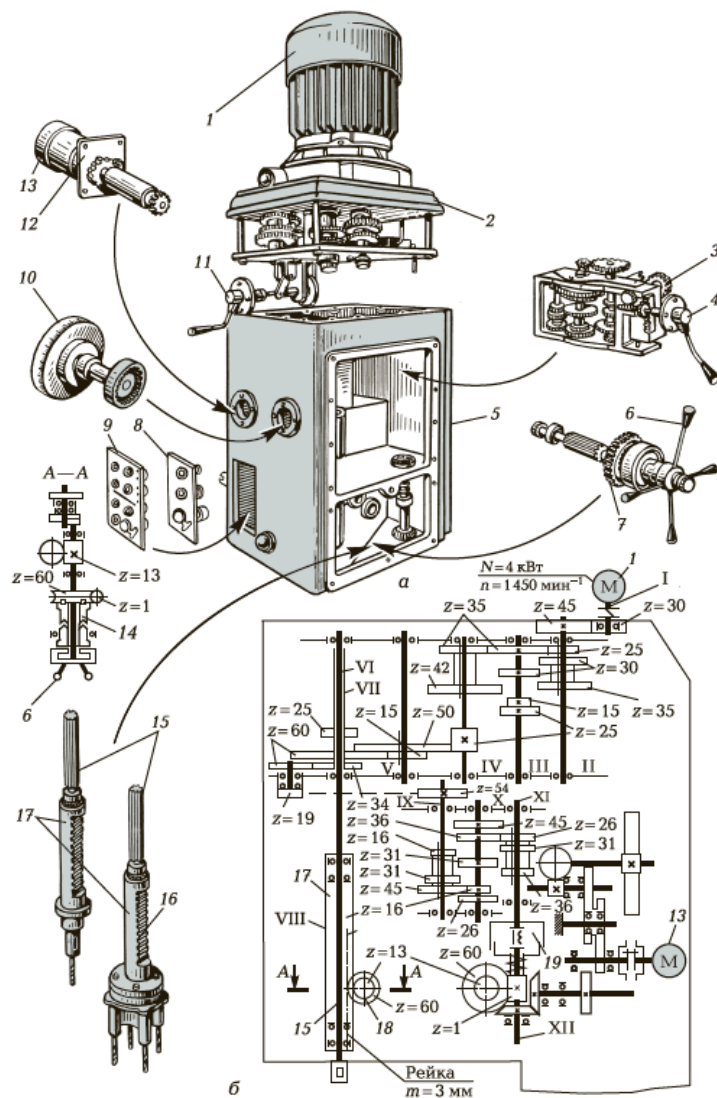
Сверлильная головка (а) и кинематическая схема (б) вертикально-сверлильного станка:
